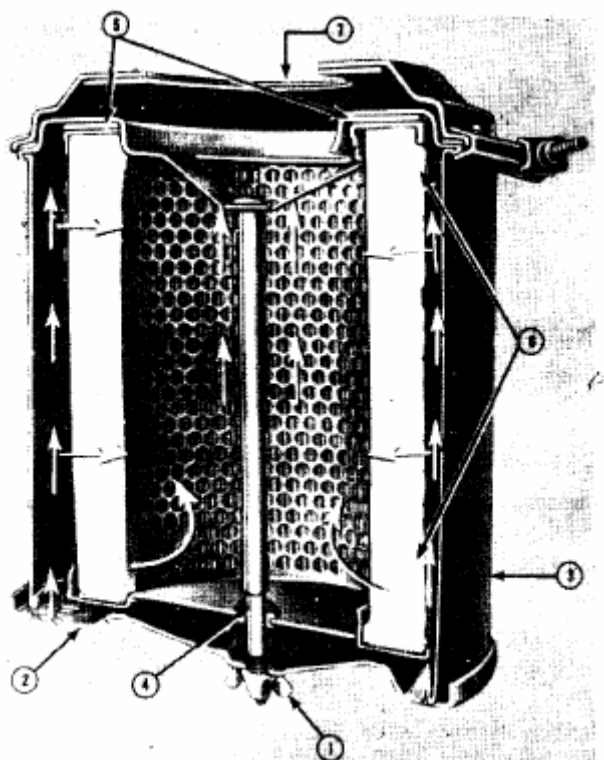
(OM1028L). Очиститель воздуха сухого типа
